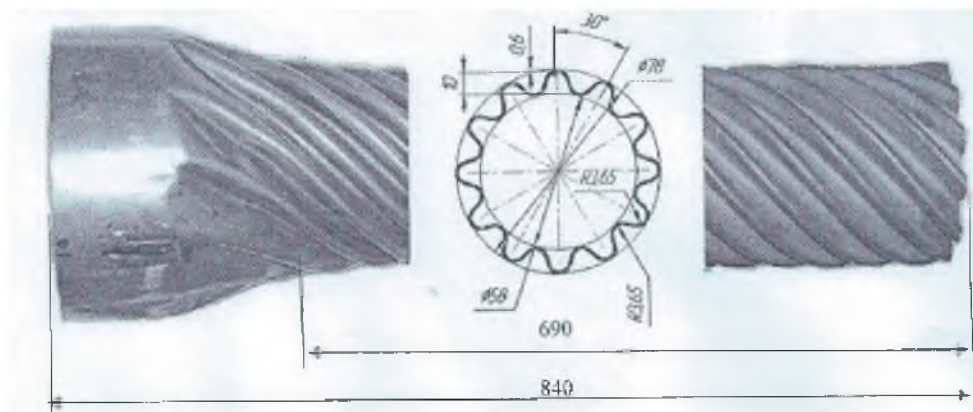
Заготовка СПТ сепаратора с закруткой потока
